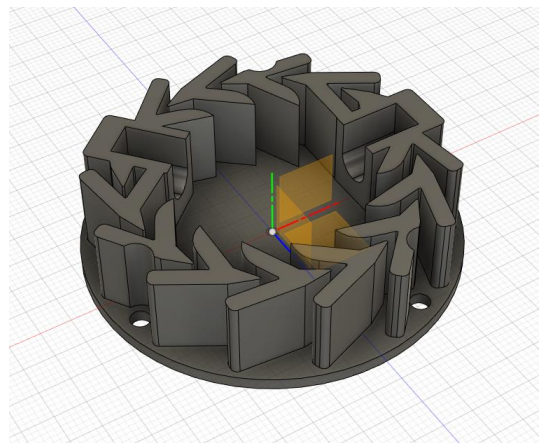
CAD-Zeichnung Gehäuse Version 2
